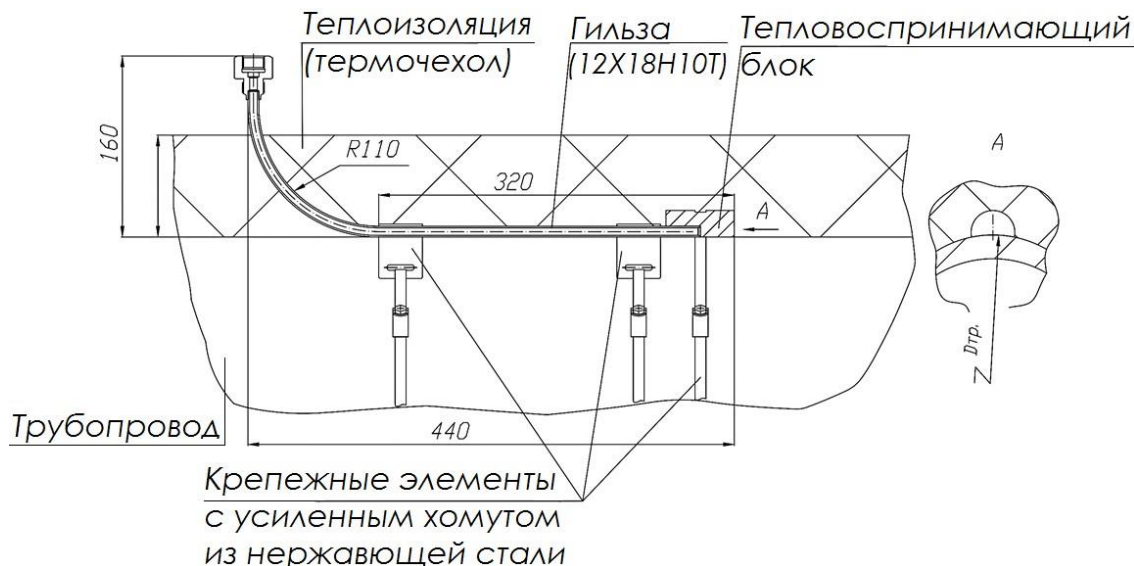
Чертеж установочного устройства РГАЖ 4.168.030-D.
